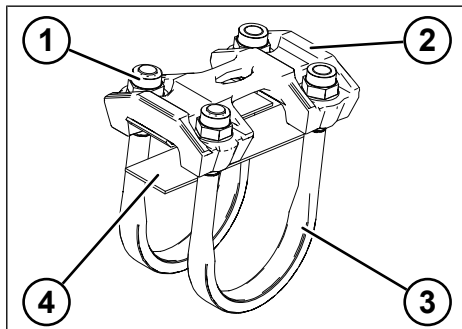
Компоненты соединительного элемента (верхний рычаг пневматической подвески)
